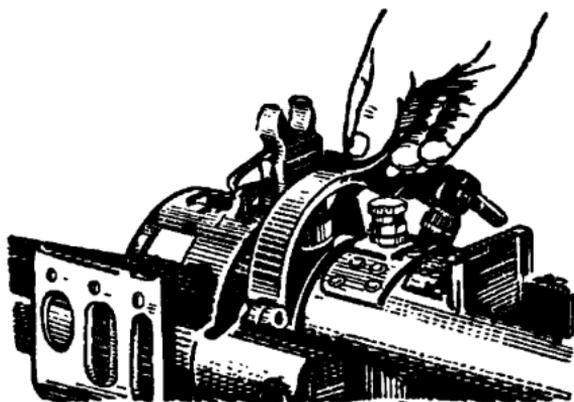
Откидывание наметки хомута крепления ствольной коробки
